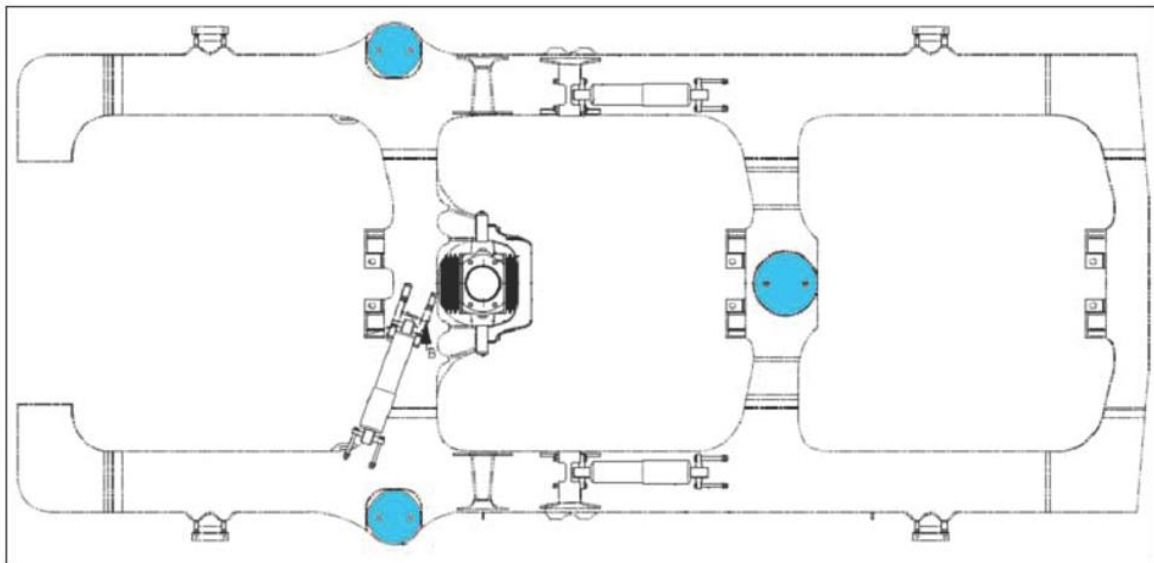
Розташування бокових опор другої ступені ресорного підвішування
